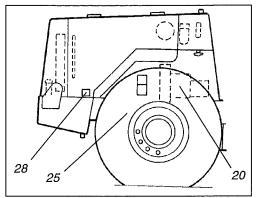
Côté droit de la machine 20 pompe hydraulique 25 essieu arrière 28 suspension du moteur
